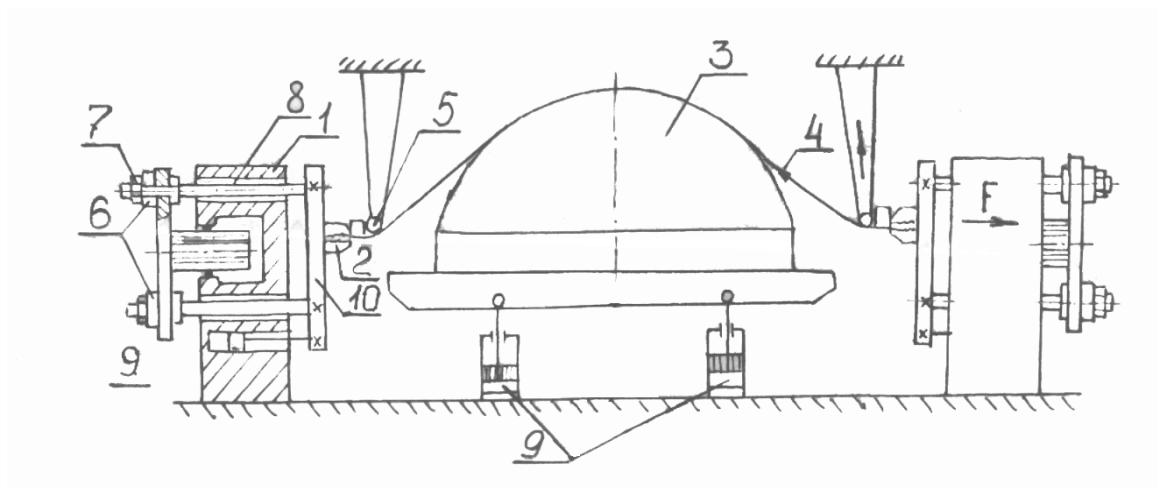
Схема обтяжки оболочки сферической формы на модернизированном прессе РО-3М после изменения силовой кинематической схемы работы
